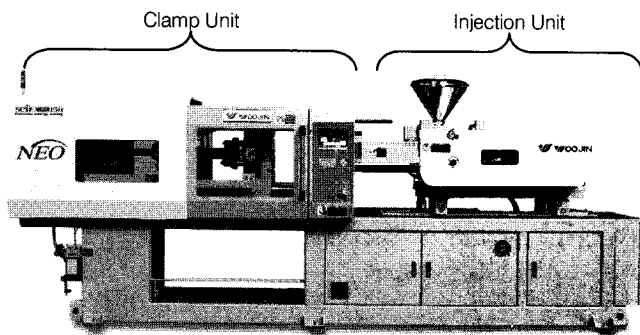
Conventional injection molding machine consisted of injection unit and clamp unit.
